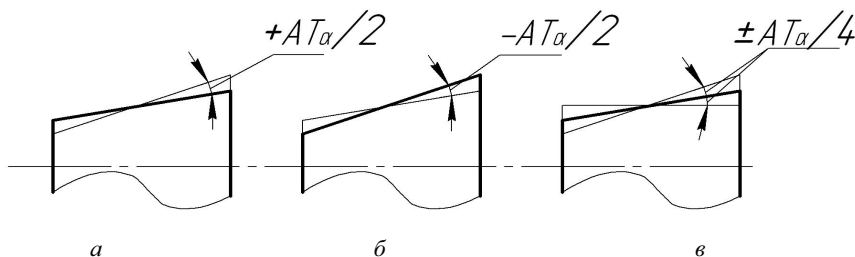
Типы расположения полей допусков для угла конуса:
